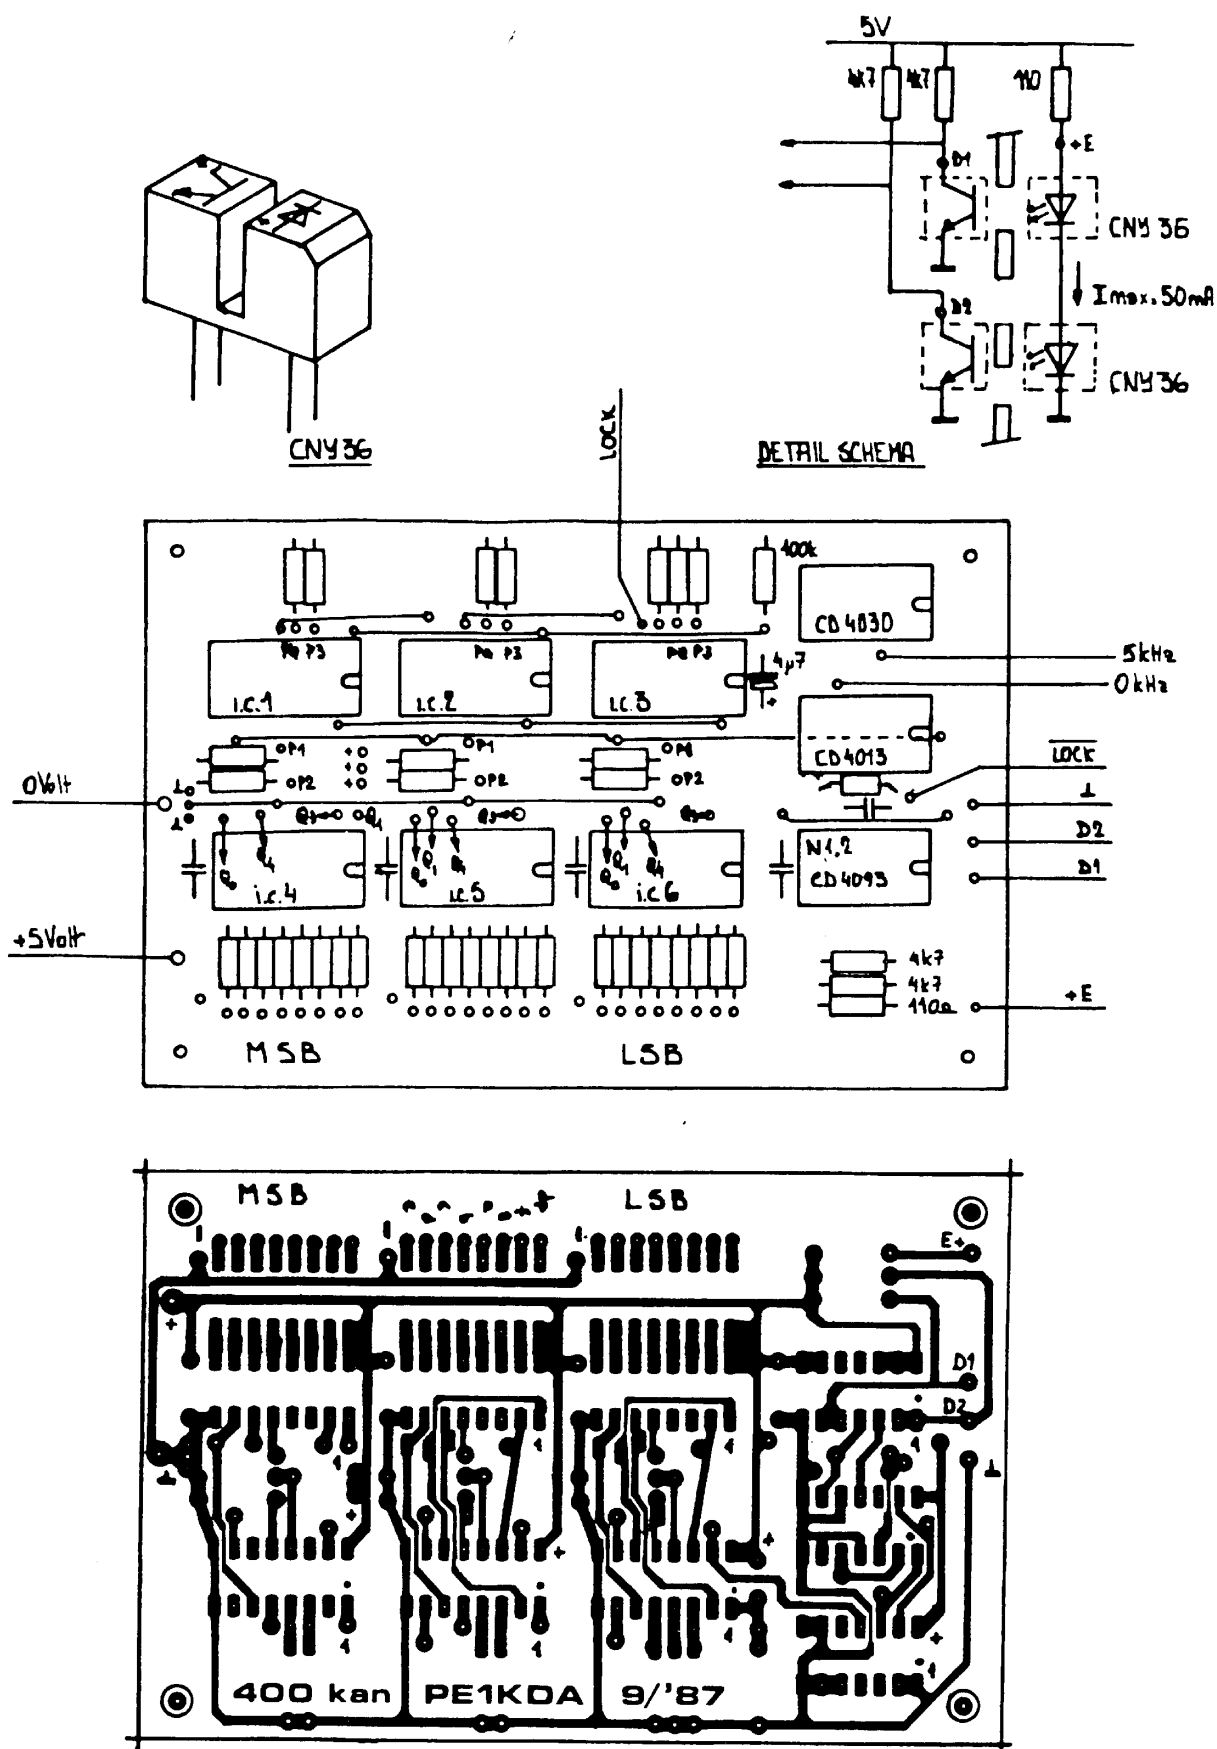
Constructie van de CNY36. Componentenopstelling en lay-out van de print.
